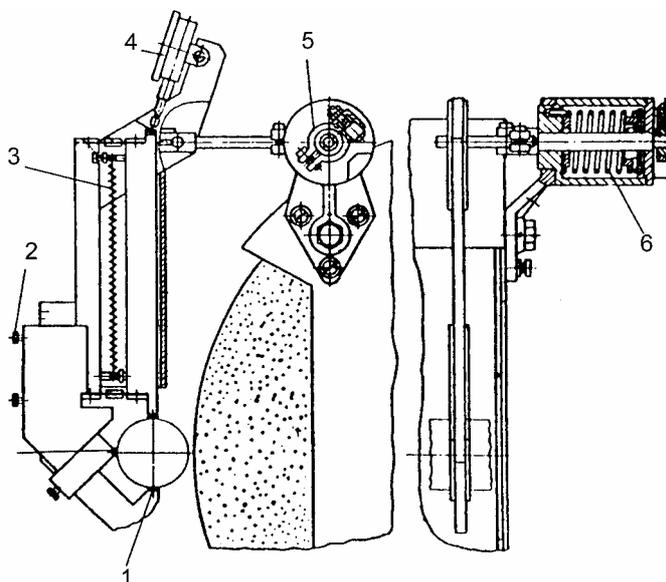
Скоба для измерения диаметра шеек валов при их шлифовании: 1 – опоры детали; 2 – винт; 3 – пружина; 4 – головка индикаторная; 5 – опора; 6 – пружина
